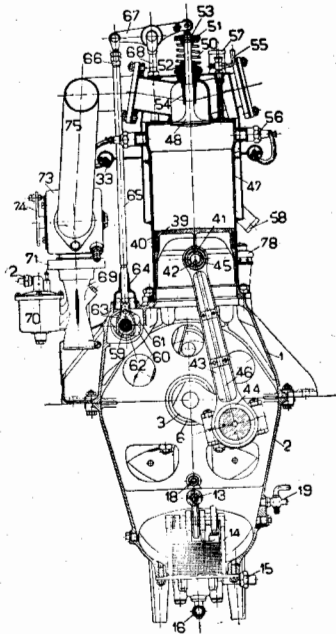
Der Argus-Flugmotor. Schnitt durch Zylinder 1.
